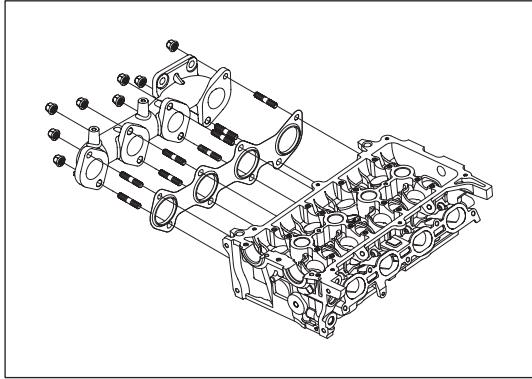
Установка выпускного коллектора с прокладкой
